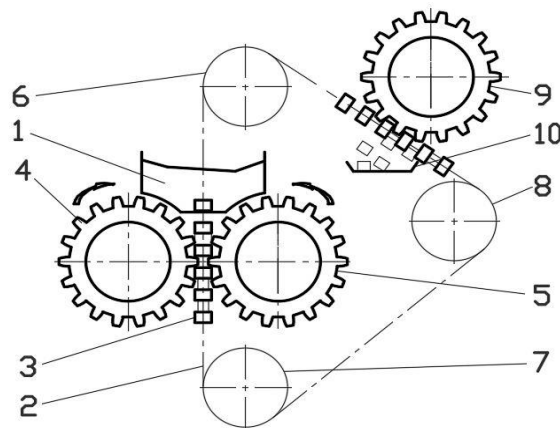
Схема пресса с зубчатыми колесами и матрицами.
